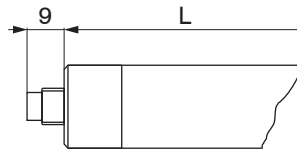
Wegsensor Typ - SA mit axialer Steckverbindung
